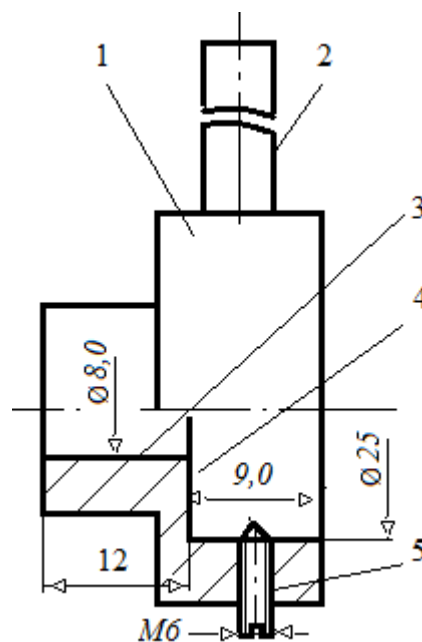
Схема плашкодержателя с направляющей частью: 1 – корпус; 2 – ручка-вороток; 3 – направляющая часть; 4 – посадочное место плашки М8; 5 – стопорный винт М6
